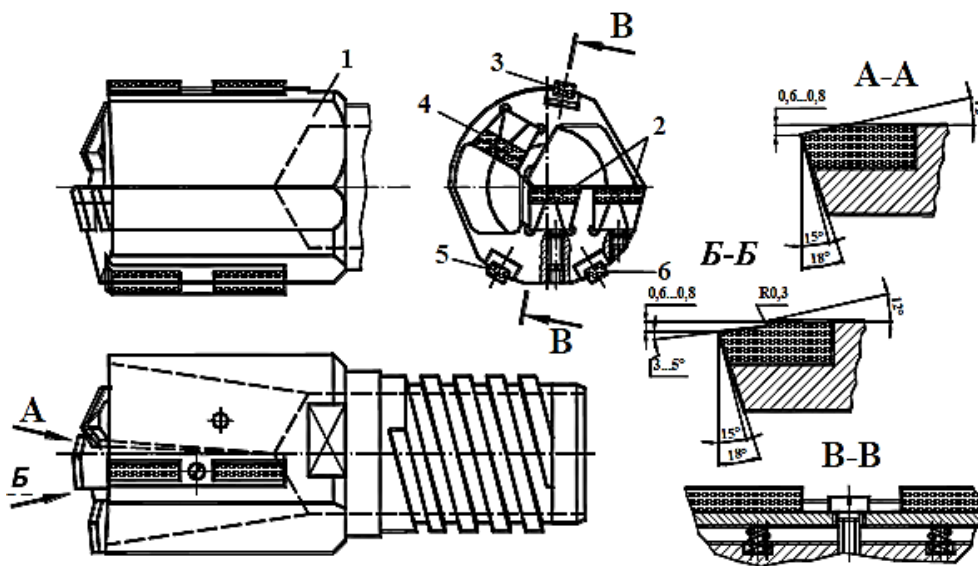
Трьох різцеве свердло зі змінними різцями. 1 - корпус; 2, 4 - різці; 5, 6 - жорсткі напрямні; 3 - підпружинені напрямні.
